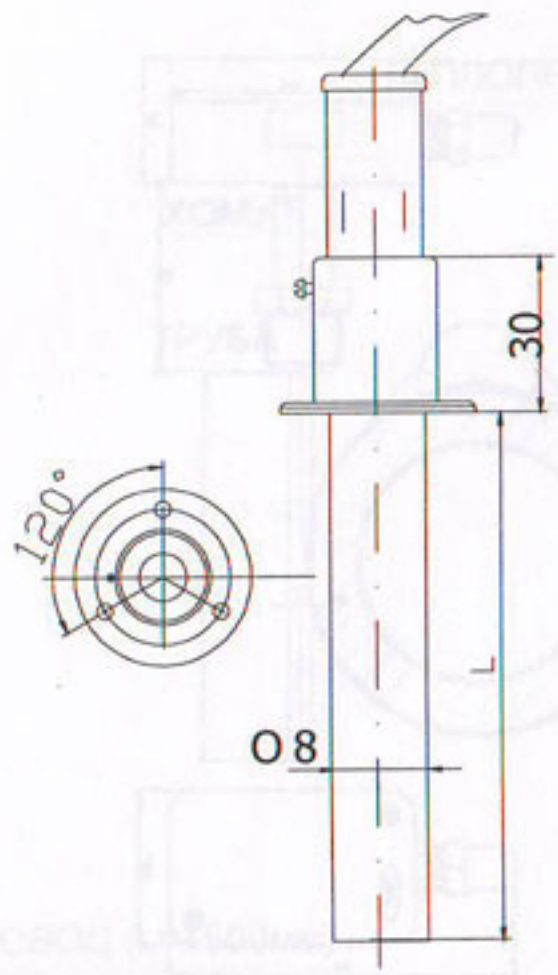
Конструктивные особенности и габаритно-присоединительные размеры датчика СТa-02
